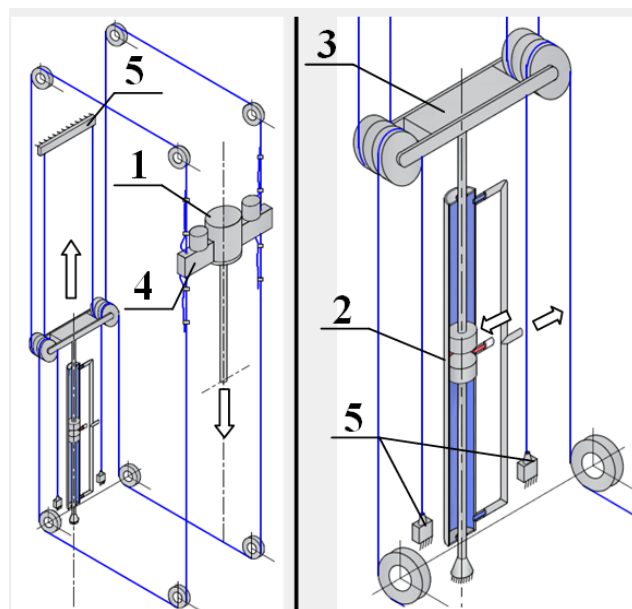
Канатно-поршневая система подачи с подвижным штоком и подвижной рубашкой гидроцилиндра станка TH-100 фирмы Ingersoll – Rand.
